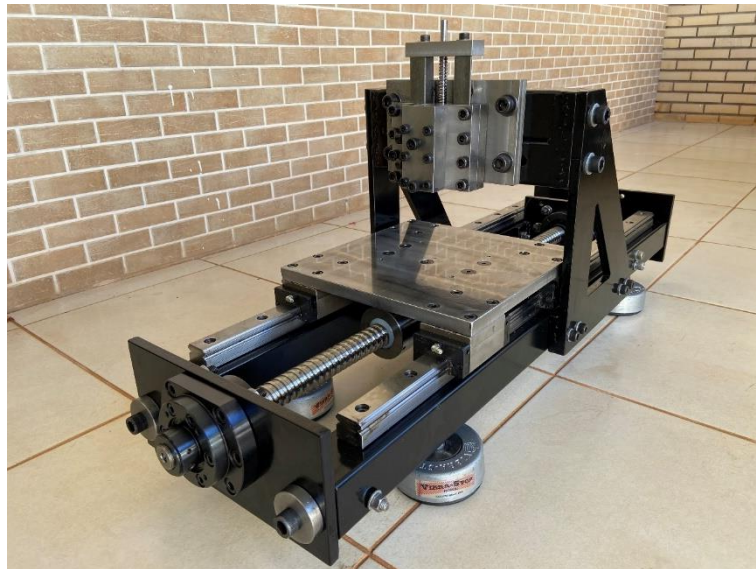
Máquina de corte ortogonal em vista isométrica.
